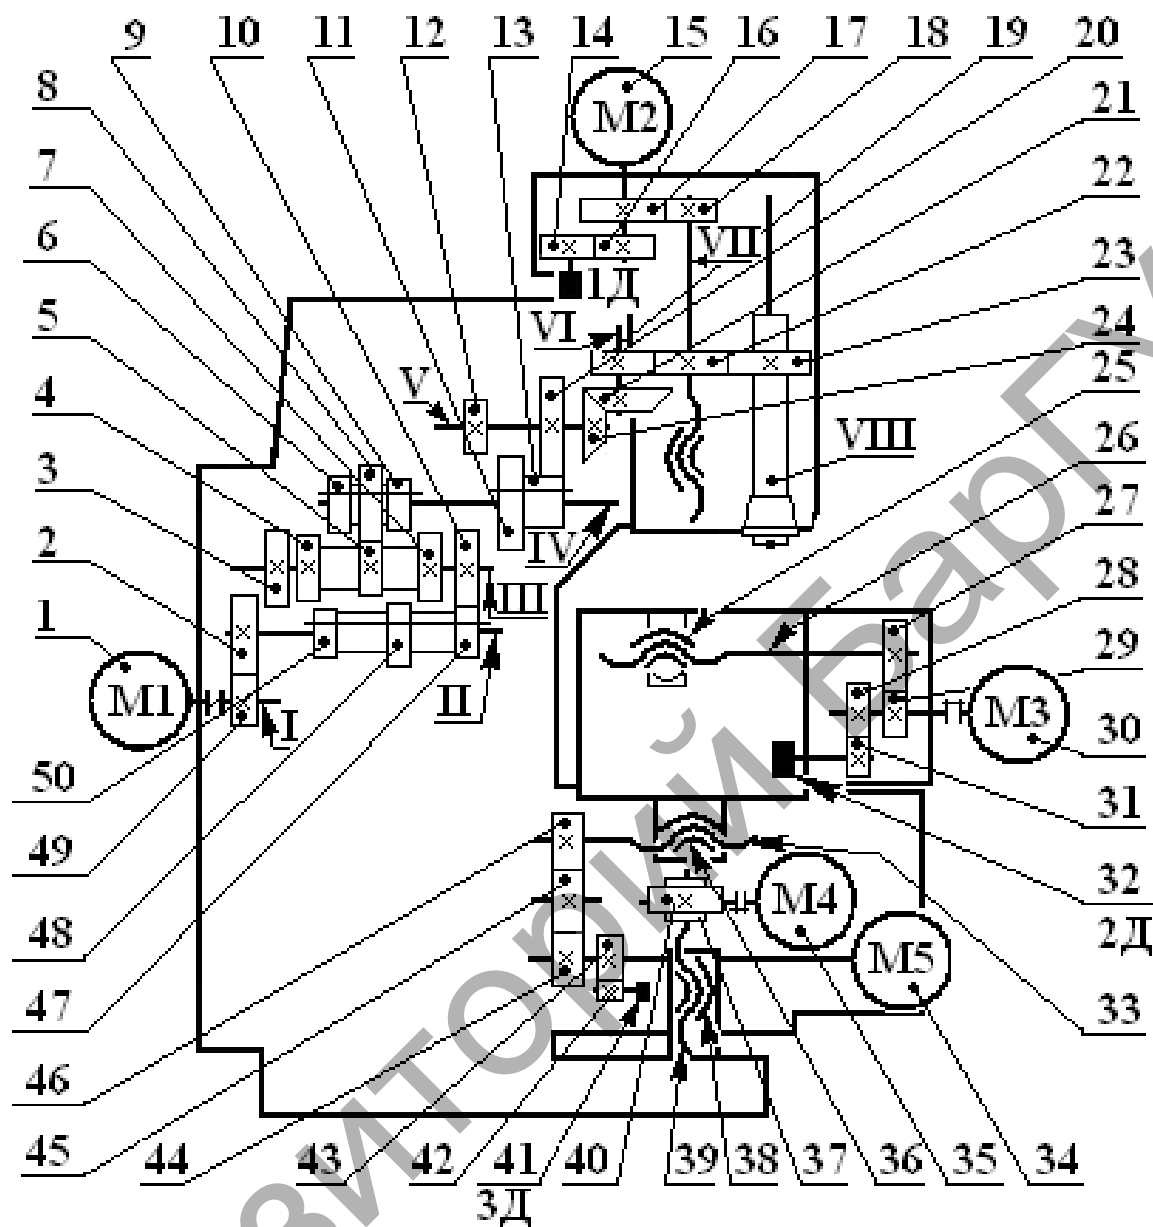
Кинематическая схема станка модели 6P13Ф3-37
